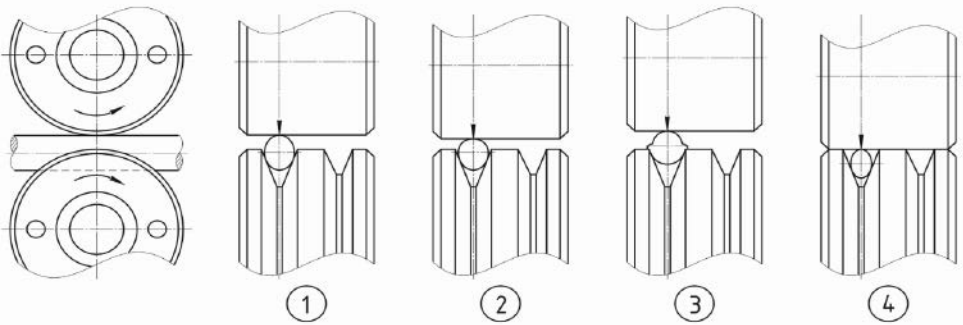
Усилие зажатия сварочной проволоки.
